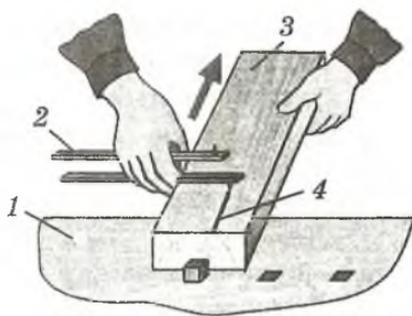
Разметка рейсмусом — по ширине: 1 — верстак, 2 — рейсмус, 3 — базовая пластина заготовки, 4 — линия разметки
